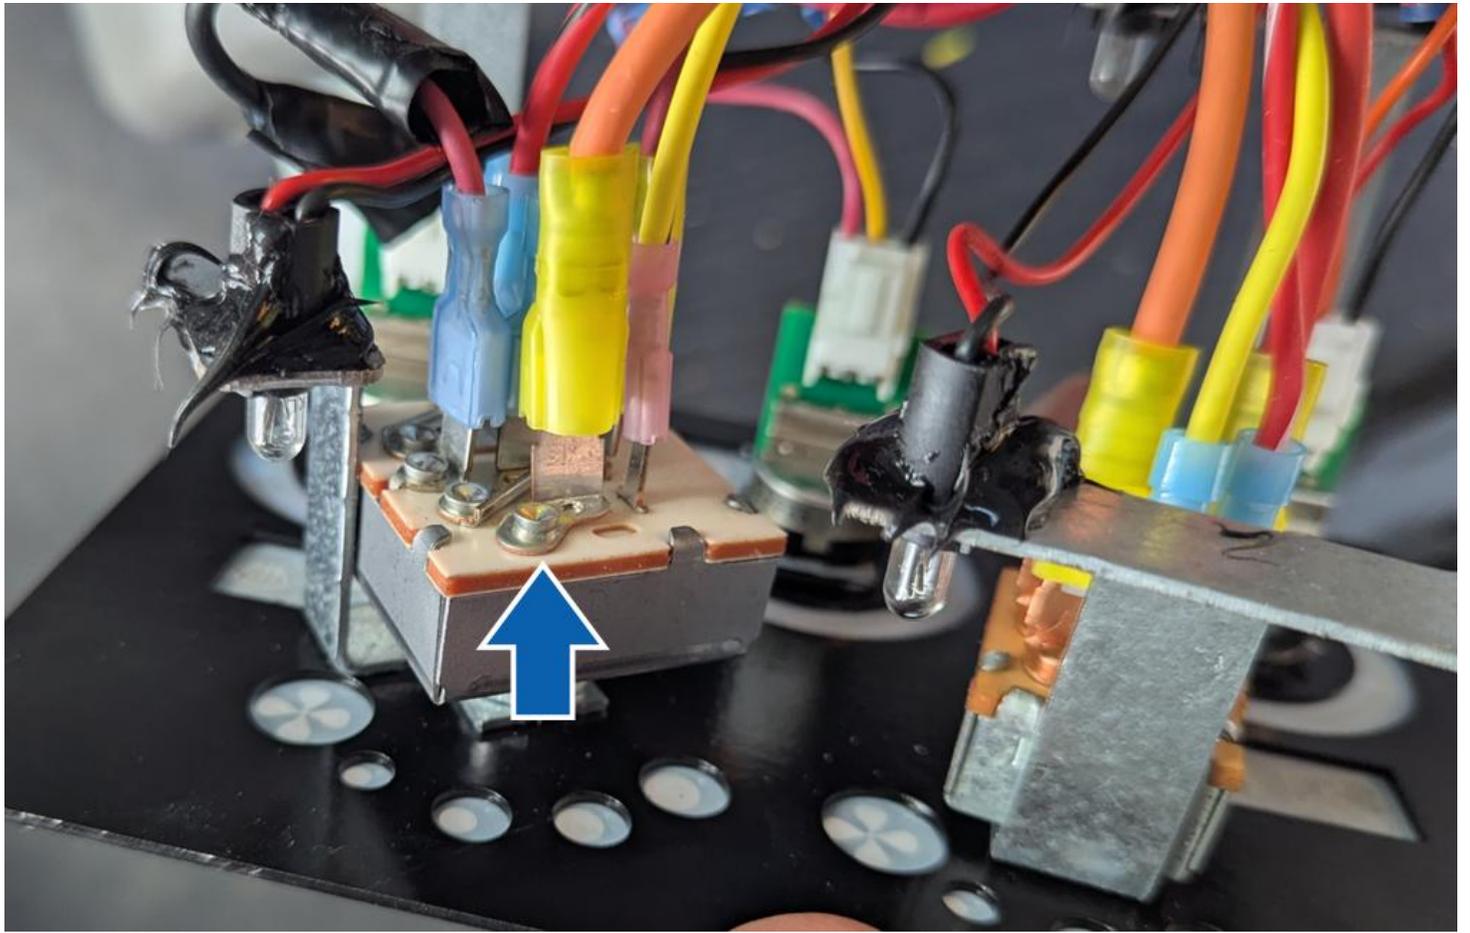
Rivets et fiches des commutateurs à inspecter.
